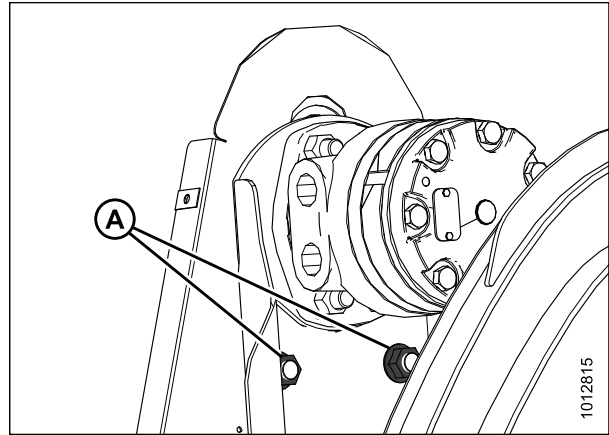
Visão do molinete simples – molinete duplo é similar
